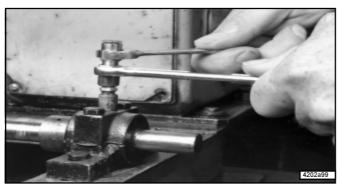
Quicklink Steckverschraubung in den Zerk-Lock-Körper einschrauben
